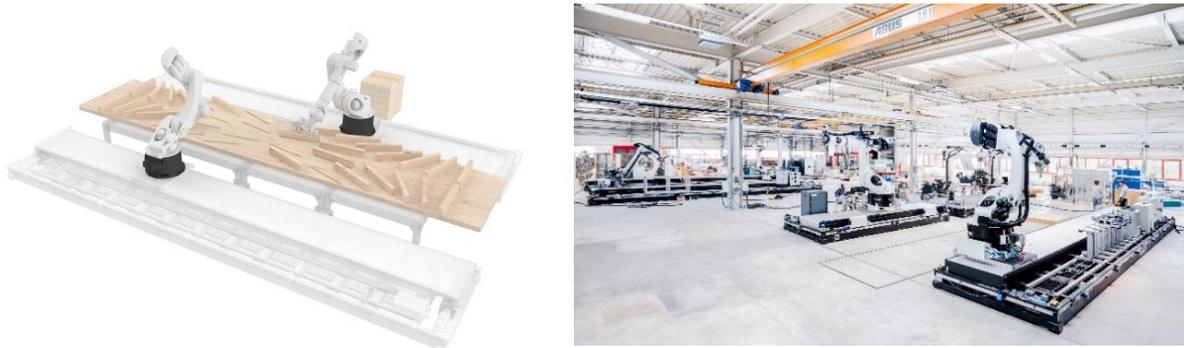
Geplante Fertigung der zweilagigen Holzdecken in der Halle des IntCDC, Waiblingen.
